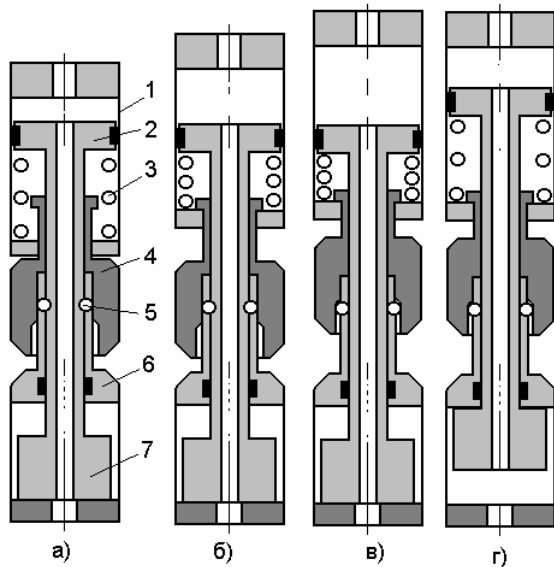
Схема ударного устройства для ликвидации прихватов бурового снаряда: 1 – корпус; 2 – ограничитель; 3 – пружина; 4 – корпус замка; 5 – шаровой замок; 6 – наковальня; 8 - боек.
